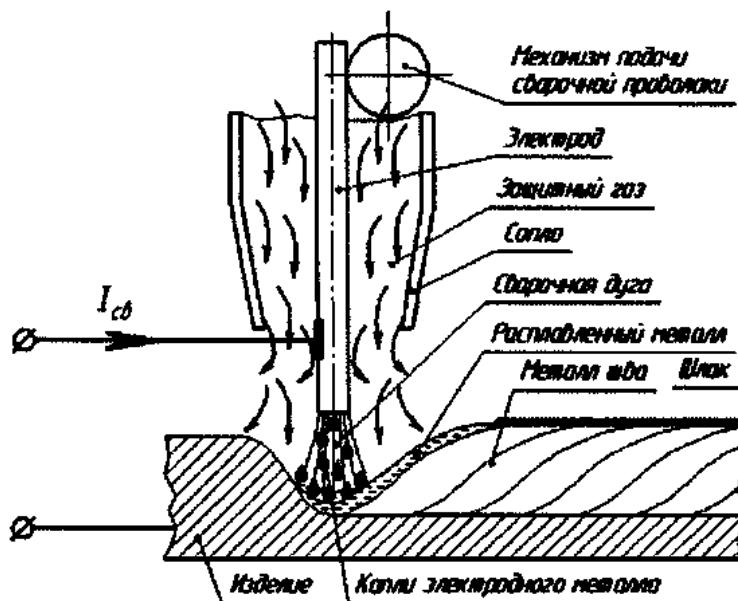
Сварка плавящимся электродом в среде защитных газов
